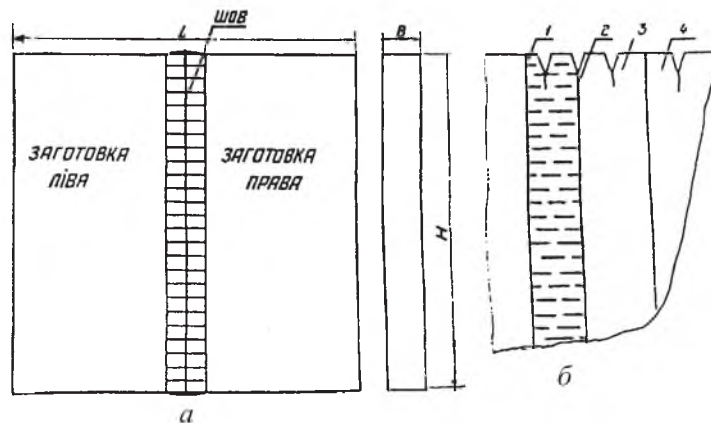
Зварювання заготовок (а) і місця виготовлення надрізів для ініціювання тріщин у лабораторних зразках зі зварним з'єднанням (б): 1 – Ш; 2 – ЗС; 3 – ЗТВ; 4 – ВМ.
